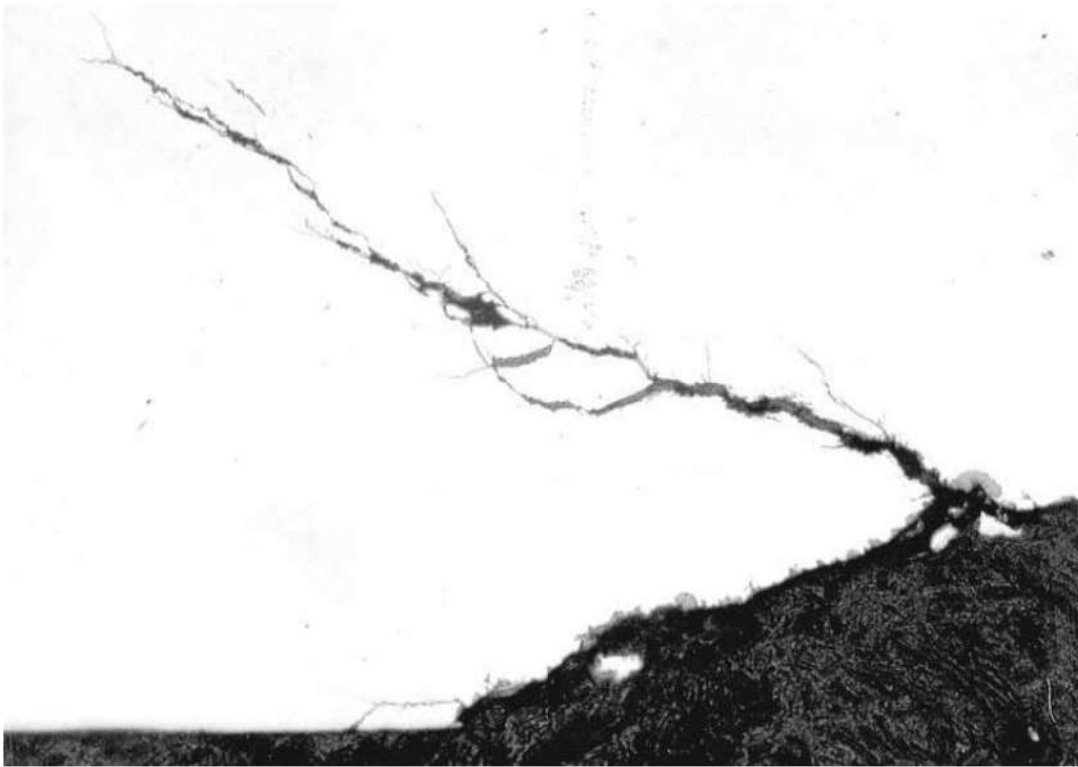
Sección transversal. Ramificación de las grietas secundarias, característico de corrosión bajo tensión. Ver detalle en la figura 15. 400X.
